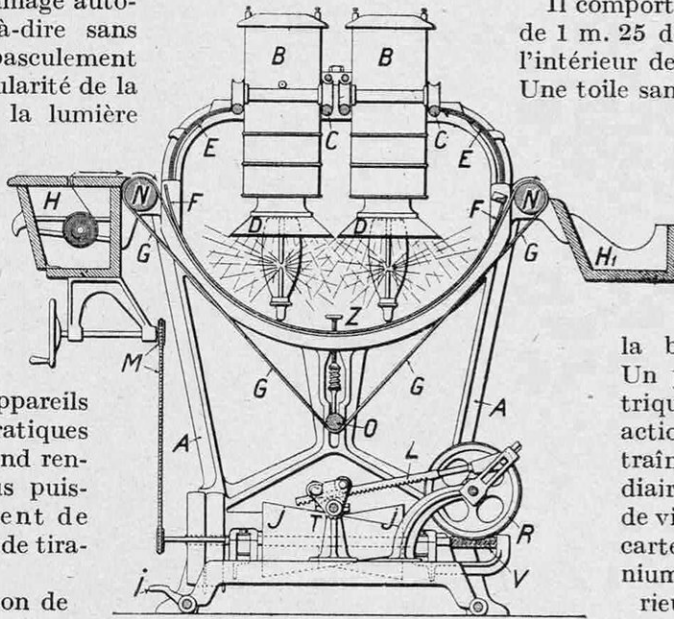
TYPE DES MACHINES MORIN ET HAUSSAIRE
